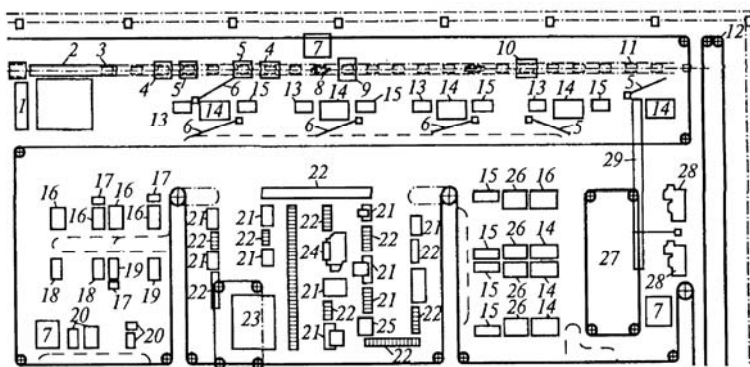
Планировка участка сборки силовых агрегатов:
